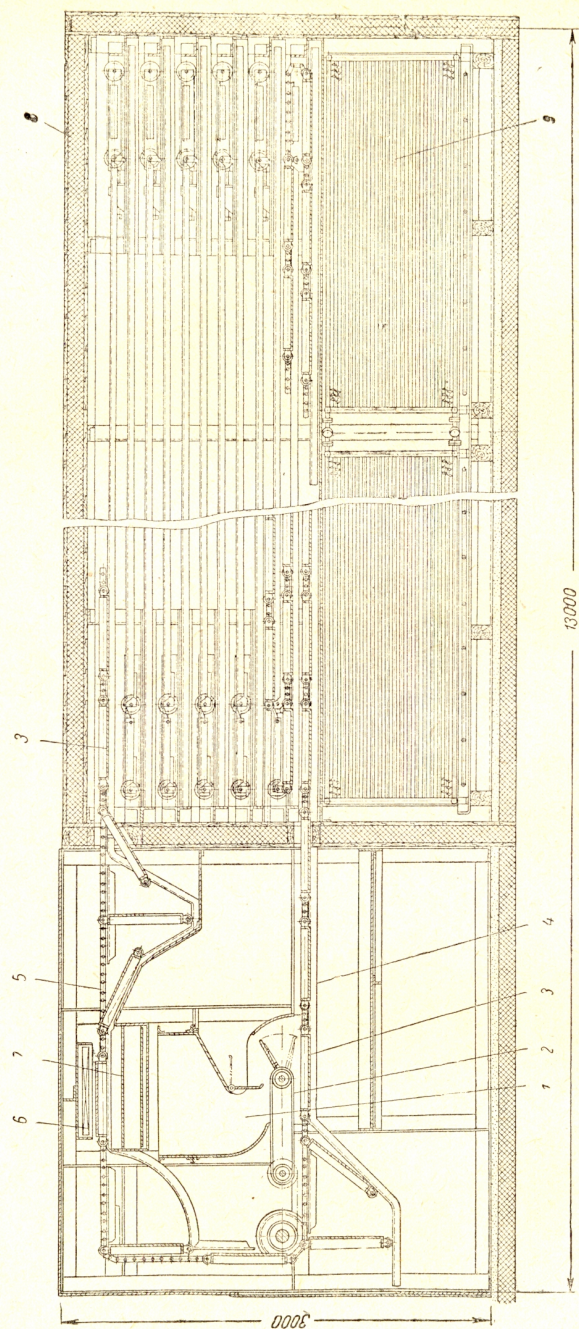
Конвейерный механизированный скороморозильный аппарат с поперечно-точным движением воздуха:
